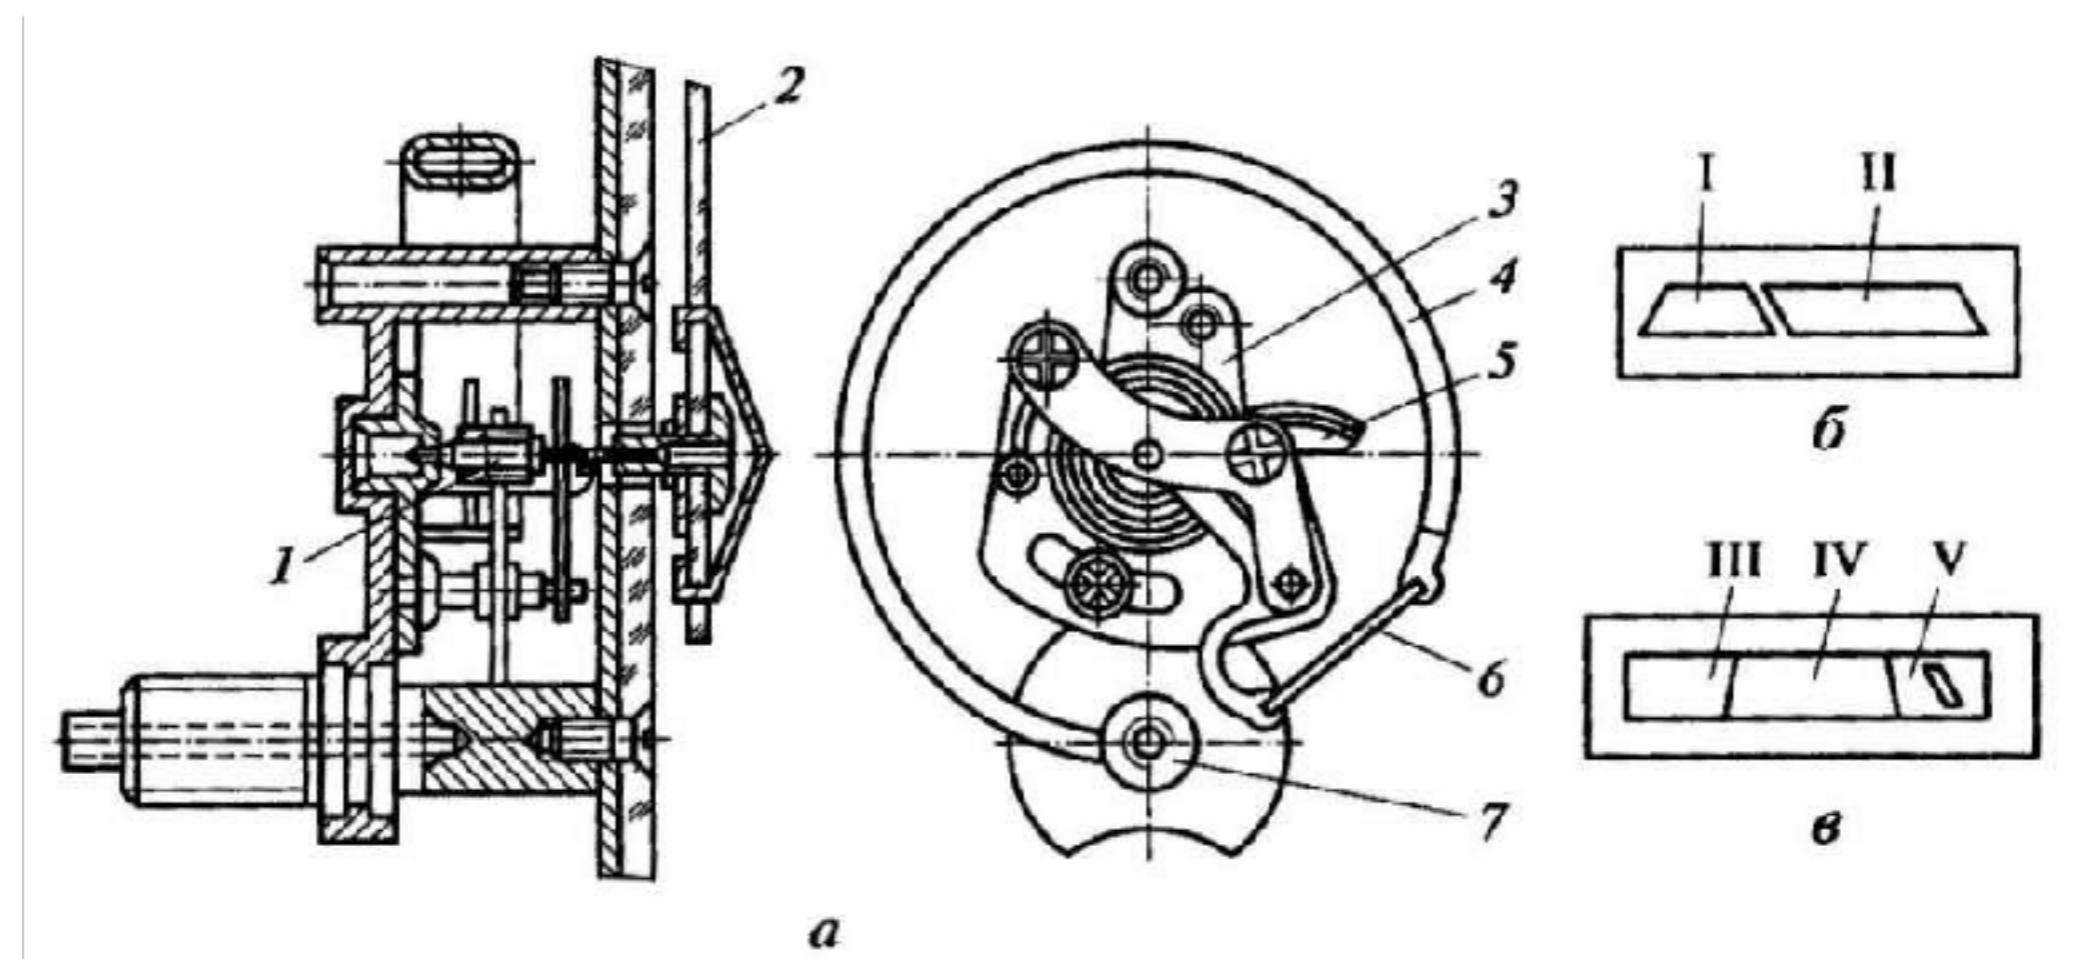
Указатель давления или разряжения с трубчатой пружиной: а — продольный разрез и вид сзади; б и в — шкалы эконометров; 1 — центрирующий узел; 2 — стрелка указателя; 3 — возвратная пружина; 4 — трубчатая пружина; 5 — зубчатый сектор; 6 — тяга; 7 — штуцер подвода воздуха; I — зона увеличенного расхода топлива; II — зона экономного расхода топлива; III — зона повышенного расхода топлива; IV — зона нормального расхода топлива; V — зона повышенного расхода топлива
